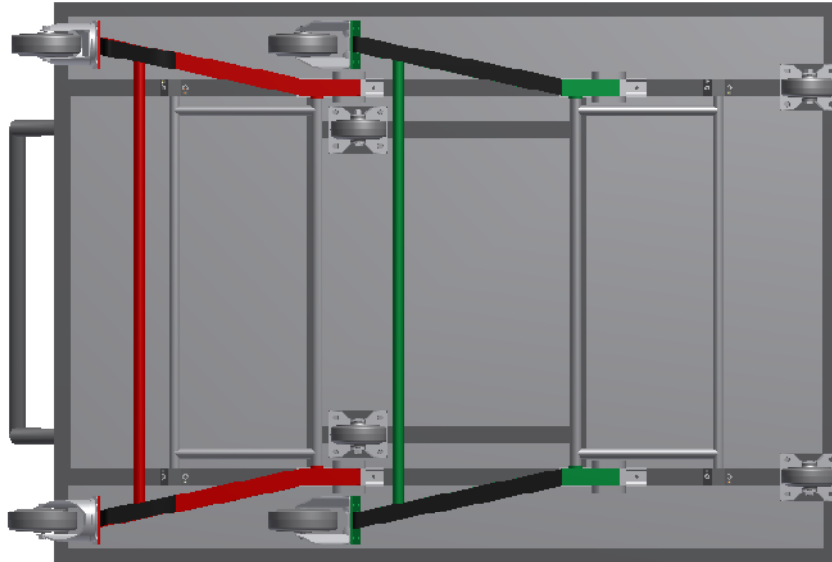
Vista de baixo do equipamento com as pernas rebatidas
